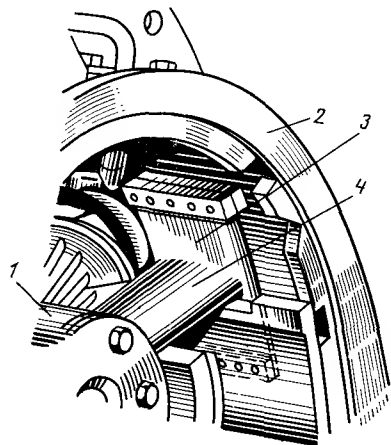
Крепление корпуса подшипника ГТУ ТЕ фирмы Рустон
